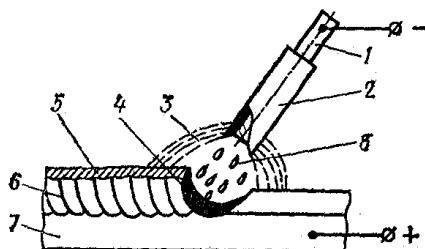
Ручне дугове зварювання металевим електродом з покриттям: 1 – стержень електрода; 2 – покриття; 3 – газовий захист; 4 – зварювальна ванна; 5 – шлак; 6 – метал шва.
